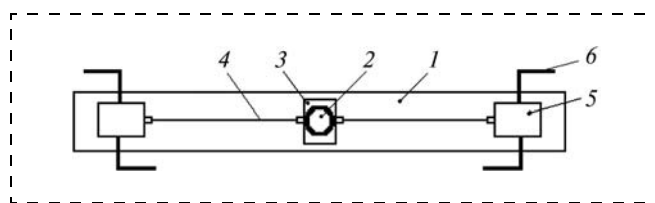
Схема привода шагающей опоры (вид сверху): 1 — несущая балка; 2 — электродвигатель; 3 — мотор-редуктор; 4 — карданные передачи; 5 — редукторы шагающих движителей; 6 — ведущие кривошипы механизмов шагания
